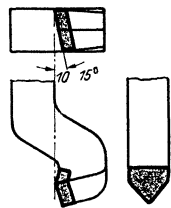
Dreh- und Hobelmeißel für schwere Schnitte.
